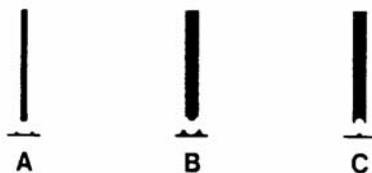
Металлические профили: А — для использования со стандартными биговальными линейками; В — С — с соответствующими биговальными линейками
